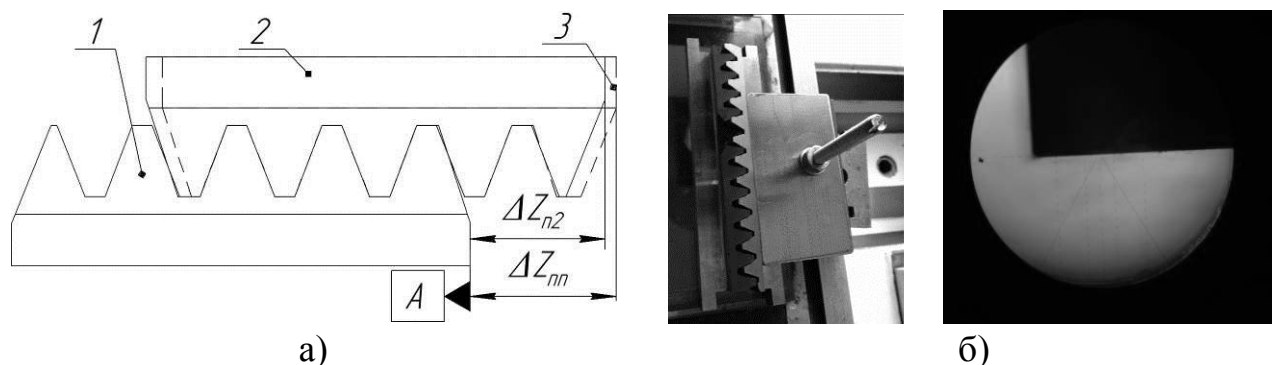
Контроль базовых торцов зубчатых реек сборной червячной фрезы:
